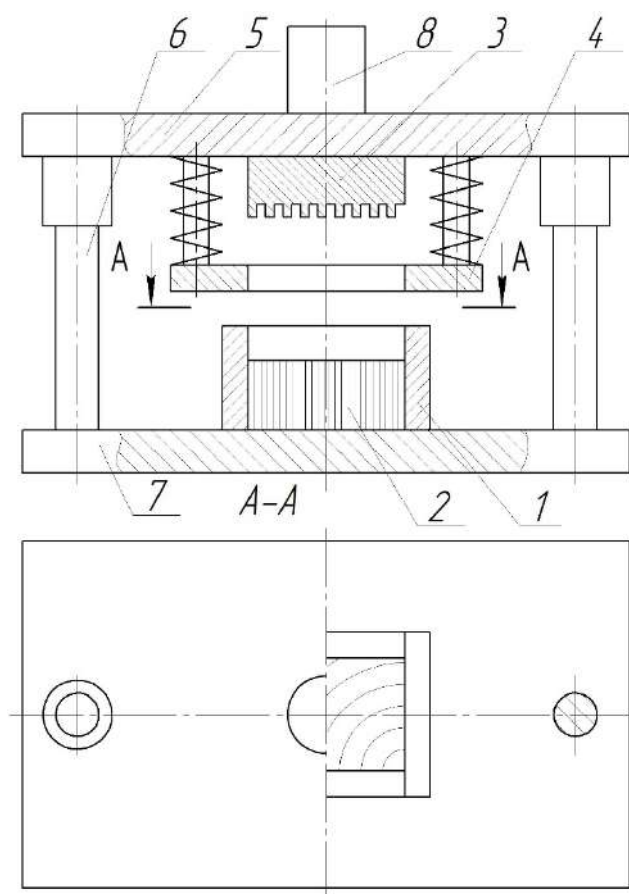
Схема предложенной конструкции штампа: 1 – матрица; 2 – заготовка; 3 – пуансон; 4 – подвижный съемник; 5 – верхняя плита; 6 – колонки; 7 – нижняя плита; 8 – хвостовик.
